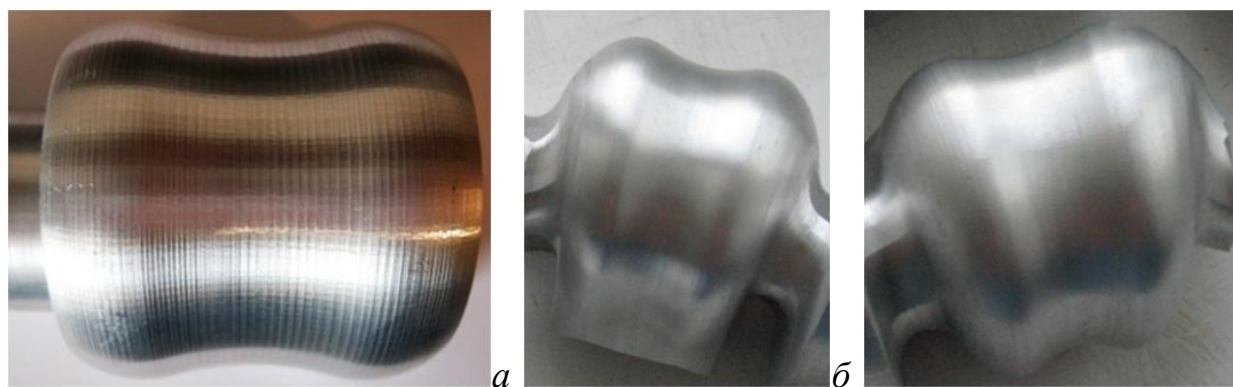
Оброблені фрезеруванням робочі поверхні протезів: сферичною (а) і циліндричною (б, в) фрезою.
